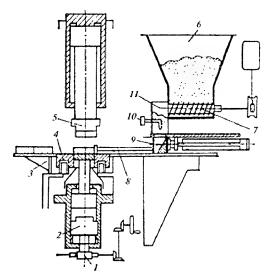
Формовочный агрегат модели ФАО-160: I— червячная пара; 2— гайка; 3— приемный столик; 4— пресс-форма; 5— верхний пуансон; 6— лвухшнековый питатель; 7— шнек; 8— упор; 9— кассета дозатора; 1θ —датчик сигнализатора уровня ЭСУ-4; II— промежуточный рукав
